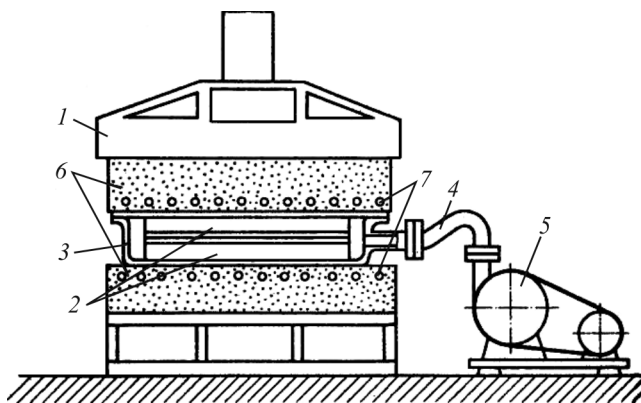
Диффузионная сварка в герметичном контейнере: 1 – плита пресса; 2 – свариваемые детали; 3 – контейнер; 4 – вакуумная трубка; 5 – вакуумный насос, 6 – нагревательные плиты; 7 – нагреватели
